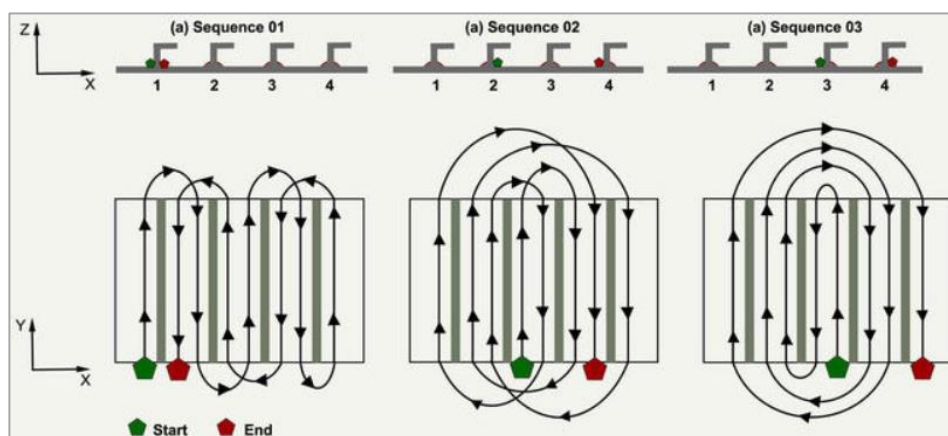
Diferentes seqüências de soldadura em painéis de aço AH32 [23]
